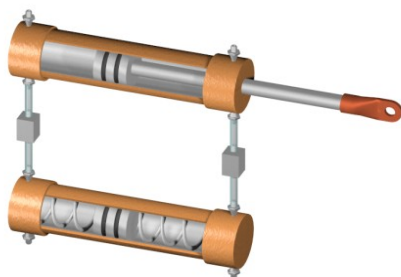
Пневмоцилиндр поршневого механизма поворота, оснащенный рекуперативно-тормозным блоком
